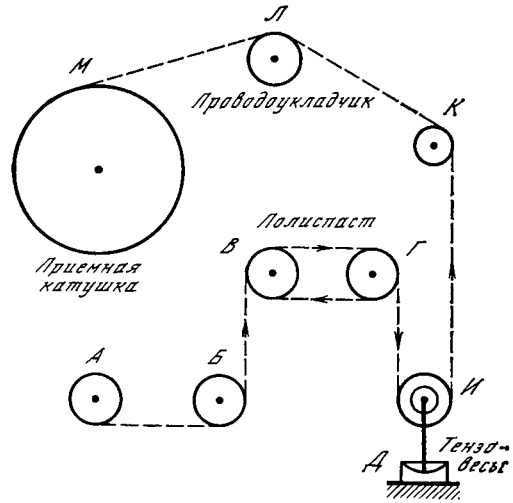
Кинематическая схема установки для намотки сверхпроводящих устройств
